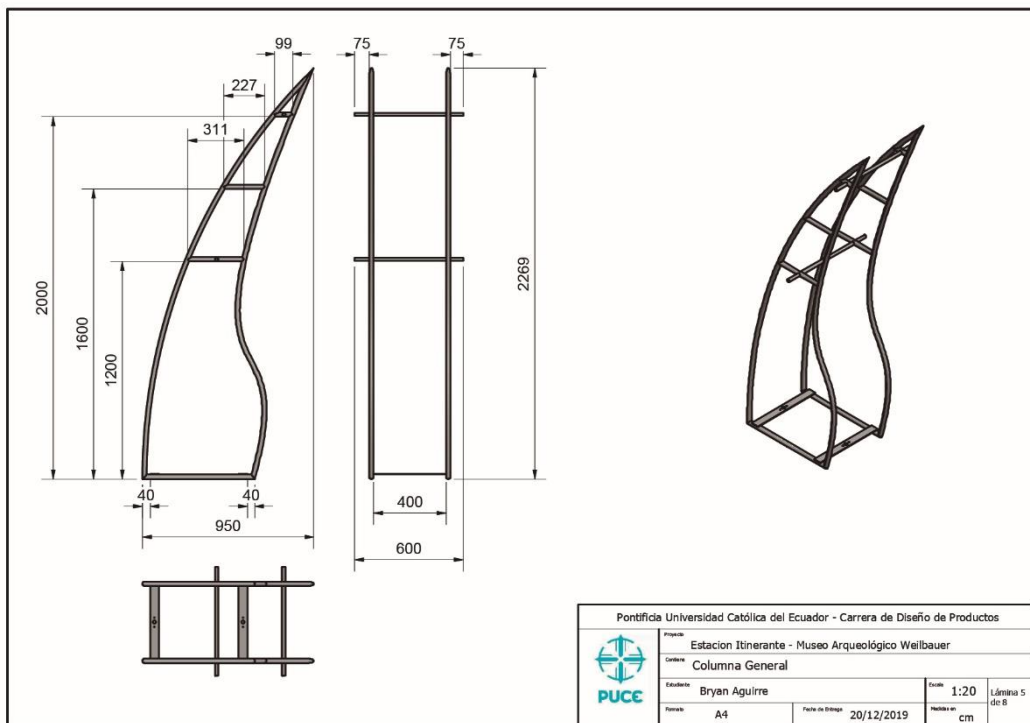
Detalle dimensional y vistas de las Columnas. Fuente elaboración propia.
